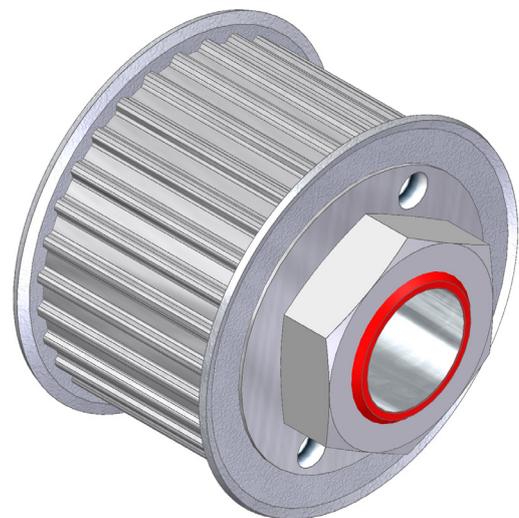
Zahnriemenscheibe mit BOQA® Befestigungselementen als einbaufertige Komplett-Baugruppe mit 2 Abdrückgewindebohrungen
